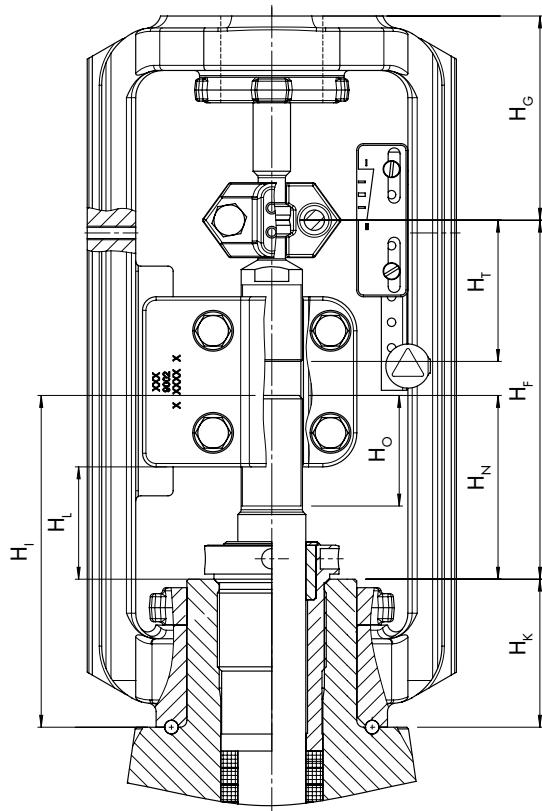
Габаритный чертёж с установочными размерами для пневматических приводов
